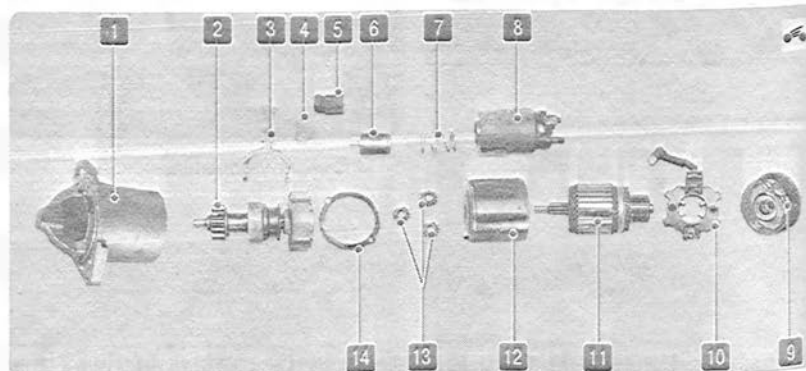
Детали стартера: 1 – крышка со стороны привода; 2 – вал привода в сборе с муфтой свободного хода и коронной шестерней планетарного редуктора; 3 – рычаг привода; 4 – опорная пластина рычага привода; 5 – опора рычага привода; 6 – якорь тягового реле; 7 – пружина тягового реле; 8 – тяговое реле; 9 – крышка со стороны коллектора; 10 – щеточный узел; 11 – ротор; 12 – статор; 13 – сателлиты; 14 – уплотнительное кольцо планетарного редуктора
